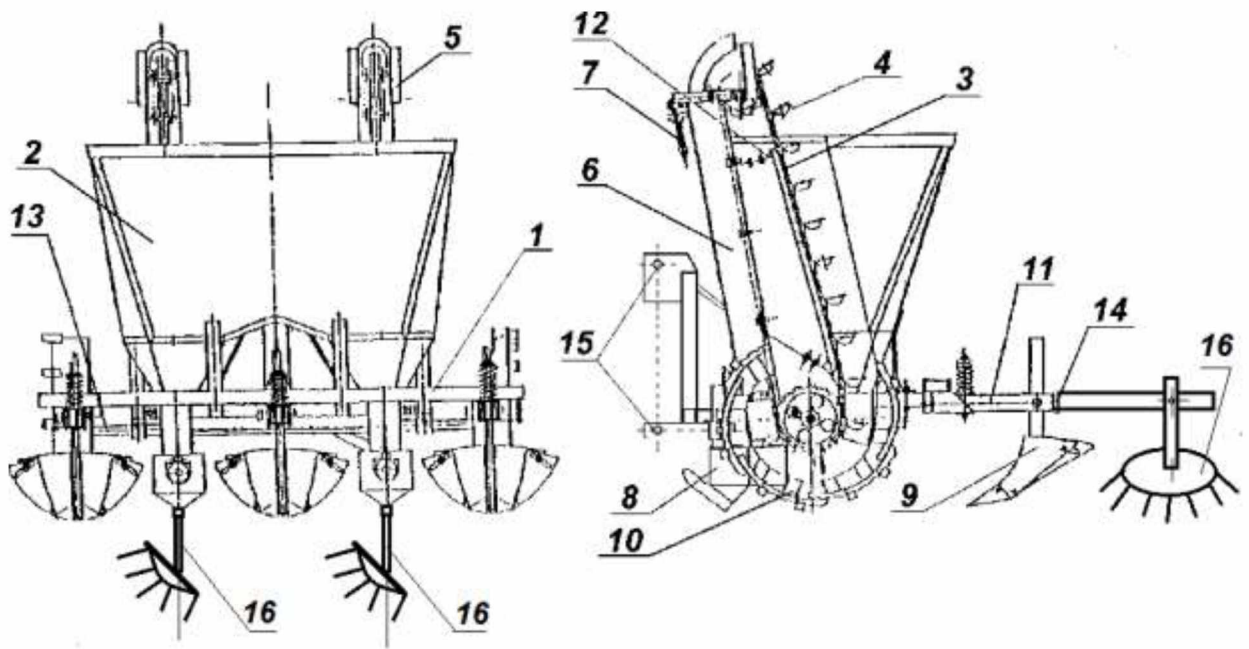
Схема дообладнання тракторної картоплесаджалки дисковими голчастими боронами: 1 – рама, 2 – бункер, 3 – ланцюговий транспортер, 4 – черпаки, 5 – садильний агрегат, 6 – зсипна труба, 7 – натяжний пристрій ланцюга, 8 – дисковий сошник, 9 – загортальна полиця, 10 – опорне колесо; 11 – важіль полиці для загортання, 12 – струшуваний агрегат; 13 – осьовий агрегат, 14 – тримачі, 15 – підвіска. [28]
